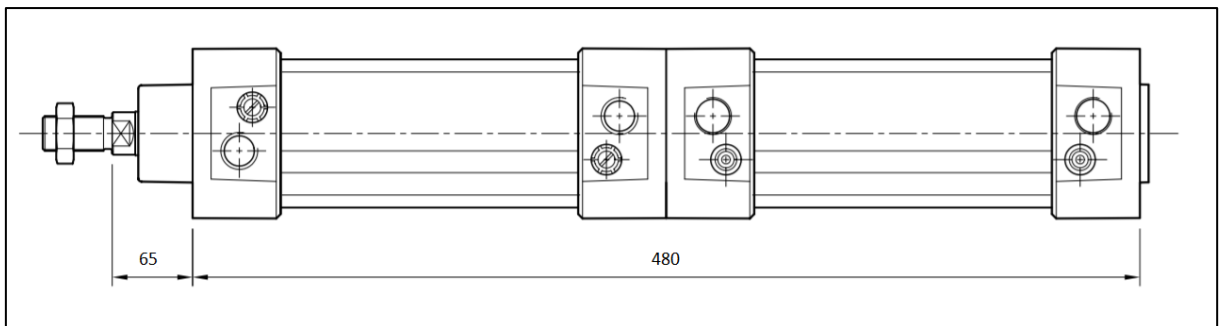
Desenho com principais dimensões do novo cilindro pneumático Tandem [20].
